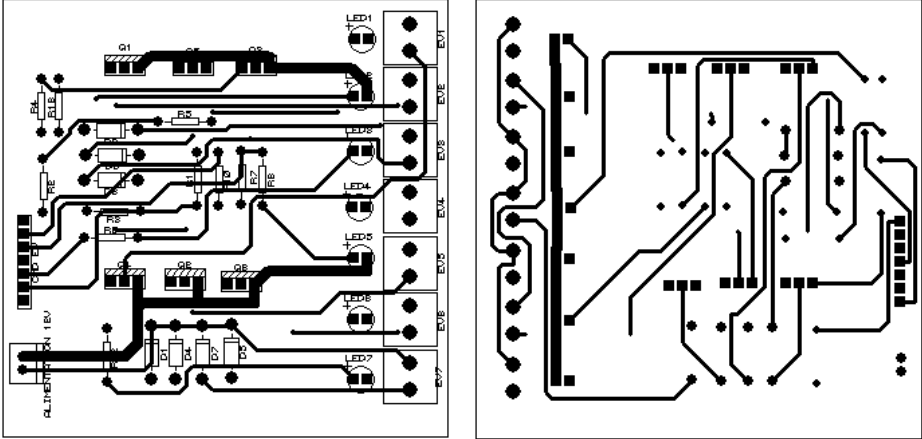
PCB TOP et BOTTOM de carte de commande +12VDC
